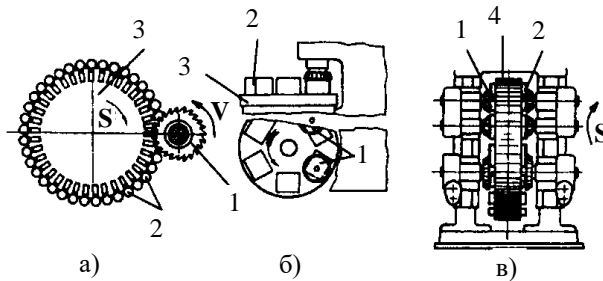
Приклади фрезерування деталей на фрезерних верстатах:
